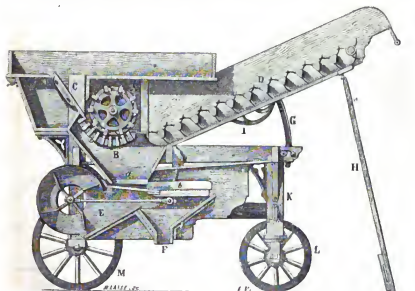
Machine à battre à grand travail de M. Cumming, à Orléans, vue en coupe.
